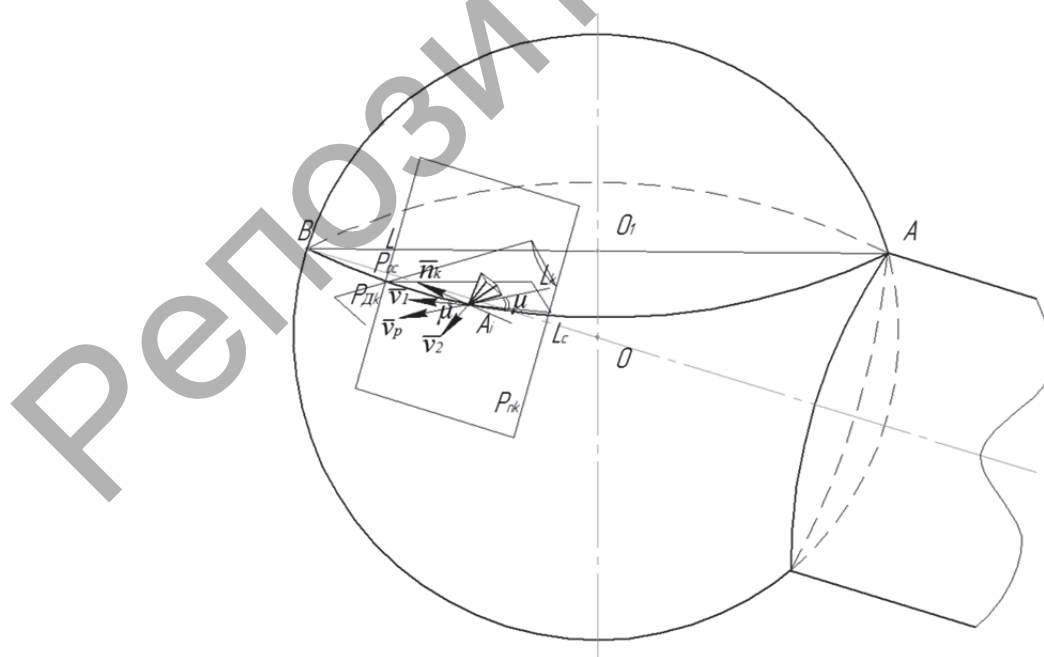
Главные статические и кинематические углы лезвия инструмента на сферической поверхности с учётом движения инструмента и заготовки
